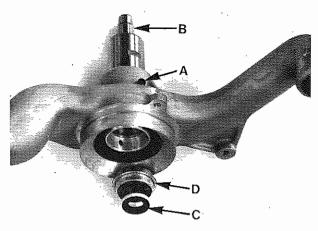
Smontaggio pompa acqua Water pump disassembly
